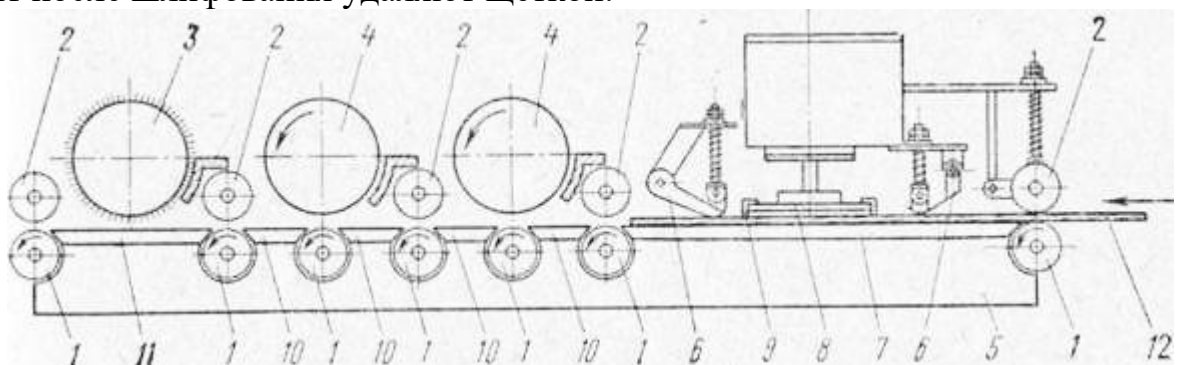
Схема обработки заготовки на фрезерно-шлифовальном станке: 1 — вальцы, поддерживающие заготовку, 2 — подающие вальцы, 3 — щетки для удаления пыли, 4 — шлифовальные цилиндры, 5 — станина, 6 — прижимы, 7, 10 и 11 — плиты станка, 8 — фрезы, 9 — ножи фрез, 12 — обрабатываемая заготовка
